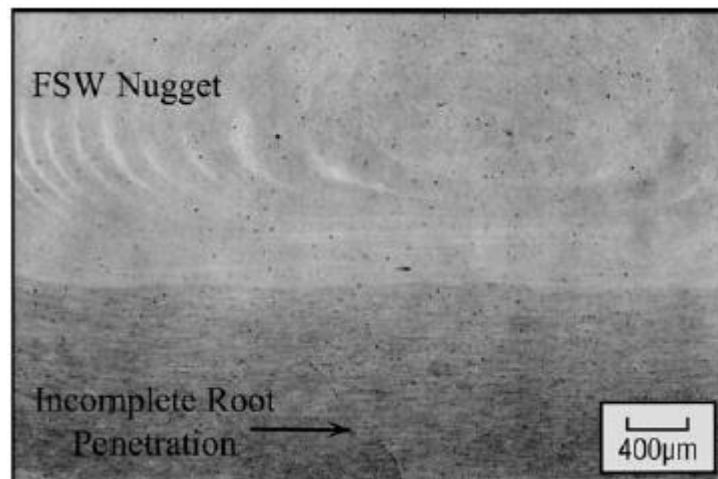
Penetração incompleta na raiz em solda por *Friction Stir Welding* mostrada por micrografia.
